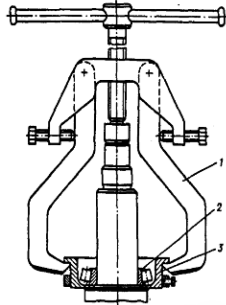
Захват для зняття внутрішнього кільця зовнішнього підшипника циліндричної шестерні середнього моста ПМ 1878-26-2: 1 – стискальні елементи; 2 – фіксатори; 3 – вал із різьбленням; 4 – ручка подачі.
